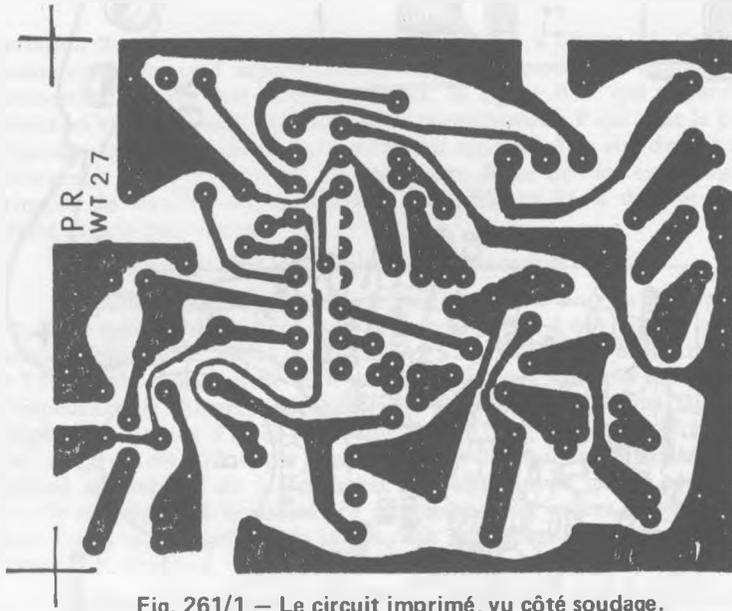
/1 – Le circuit imprimé, vu côté soudage.
